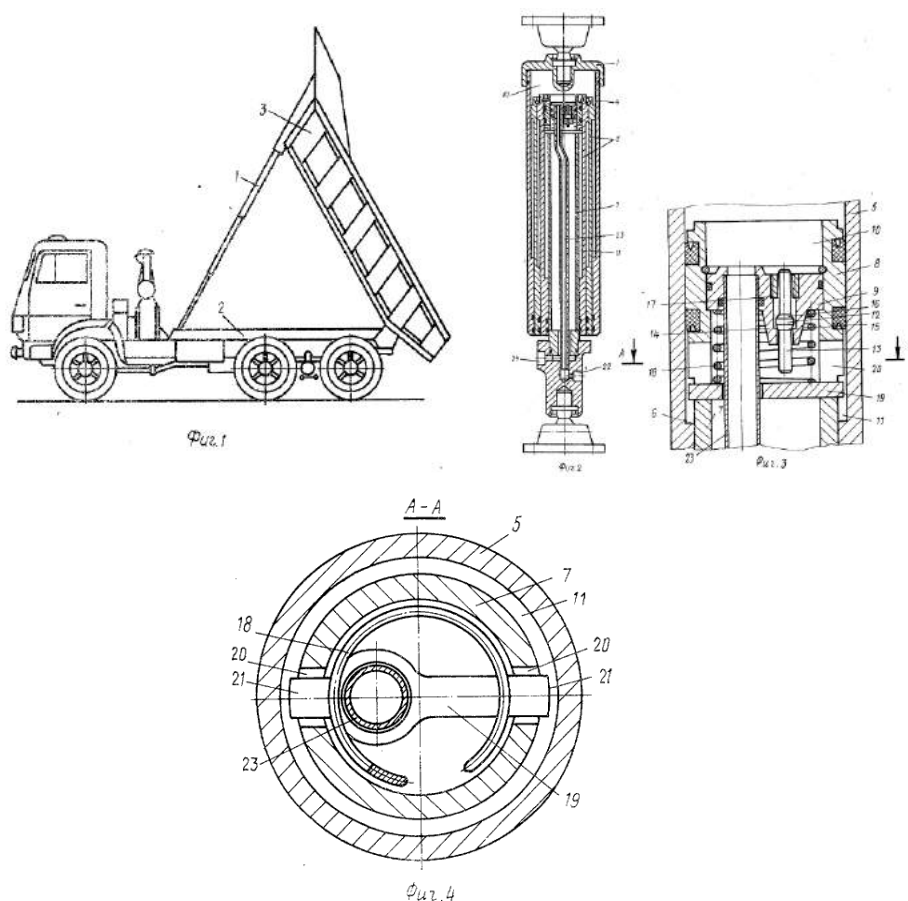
Автомобиль самосвал, на котором установлен гидроцилиндр, гидроцилиндр общий вид поршень гидроцилиндра и в разрезе А-А
